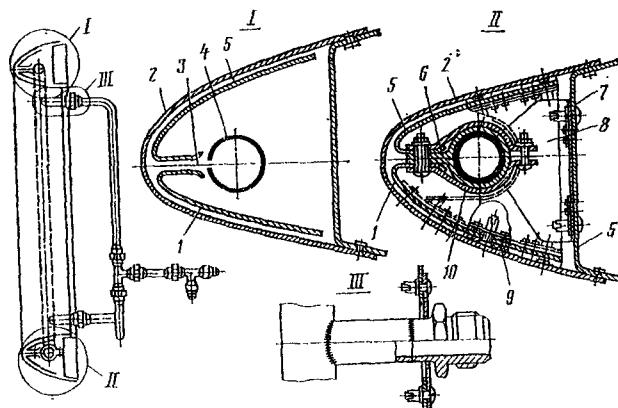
Камера микроэжекторная обогрева воздухозаборника двигателя:
